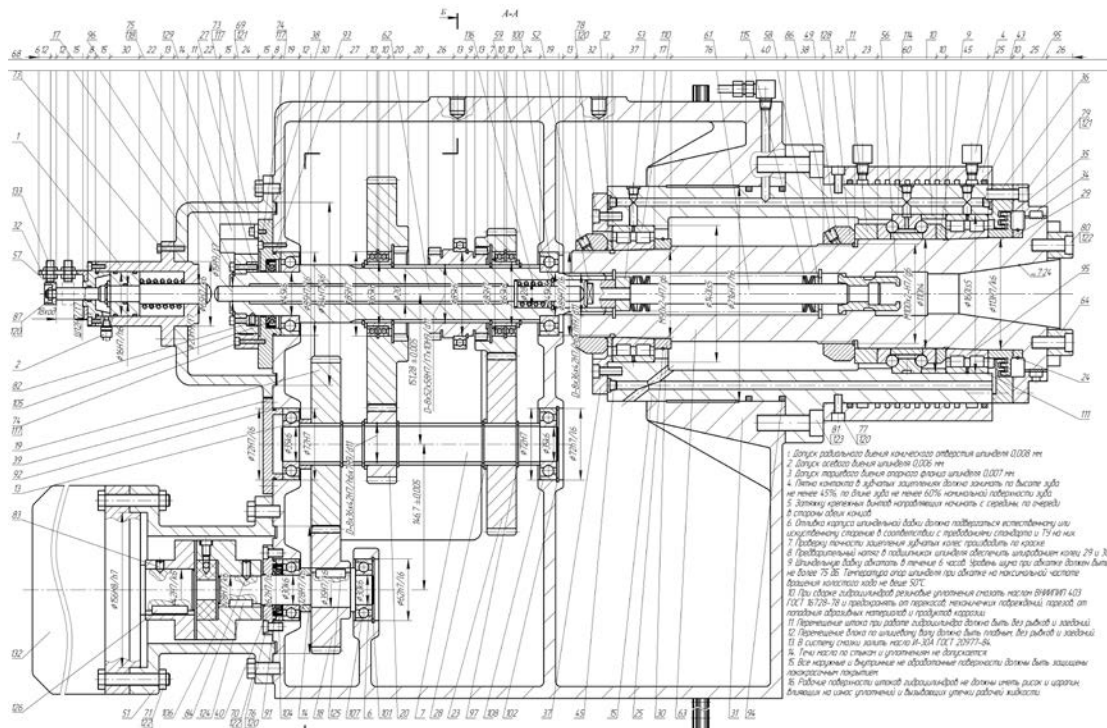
Шпиндельная бабка многоцелевого сверлильно-фрезерно-расточного станка с автономным шпиндельным узлом (развертка)
